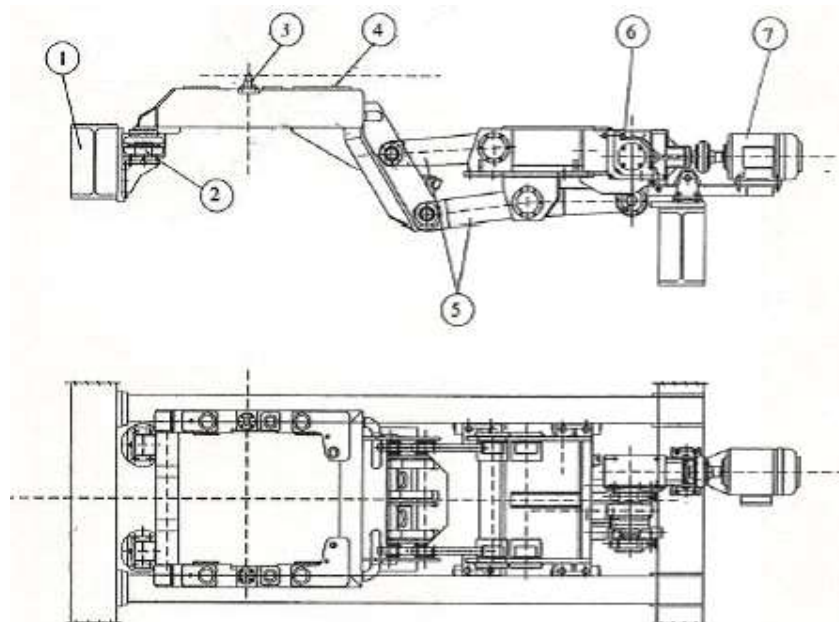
Стол качания. 1 – опорная металлоконструкция; 2 – пневмопривод; 3 – центровочный палец кристаллизатора; 4 – уровень расположения кристаллизатора; 5 – рычаги; 6 – редуктор; 7 – электродвигатель переменного тока.
